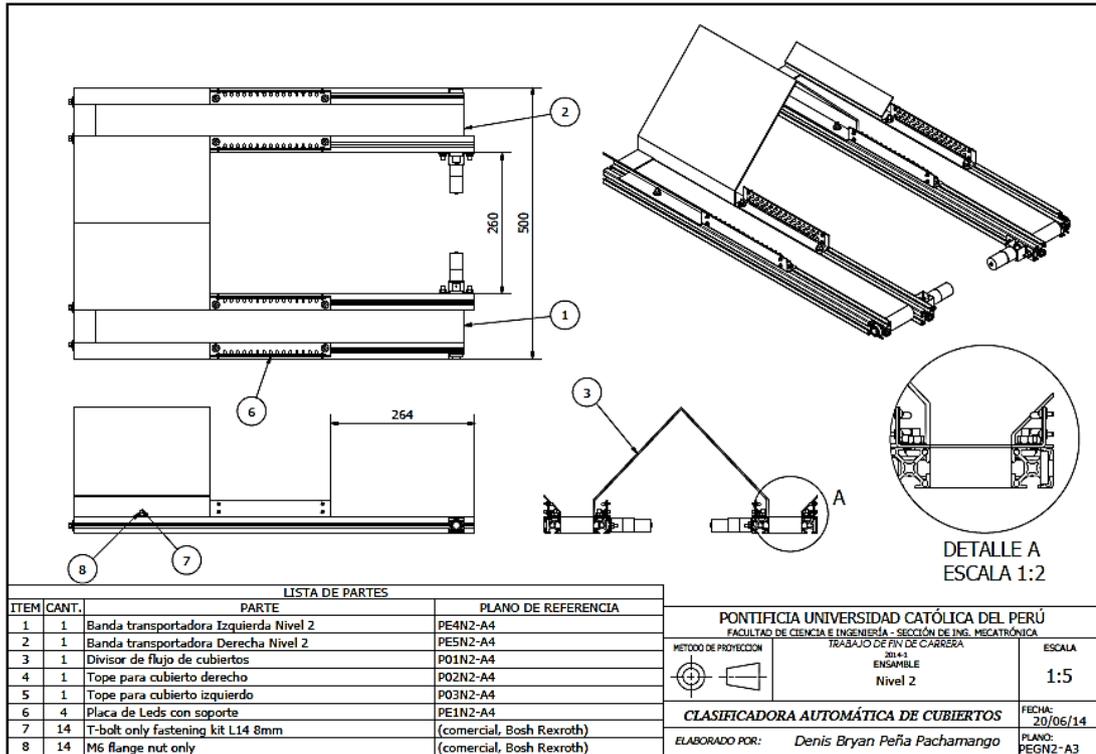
Ensamblaje Nivel 2- Parte superior
